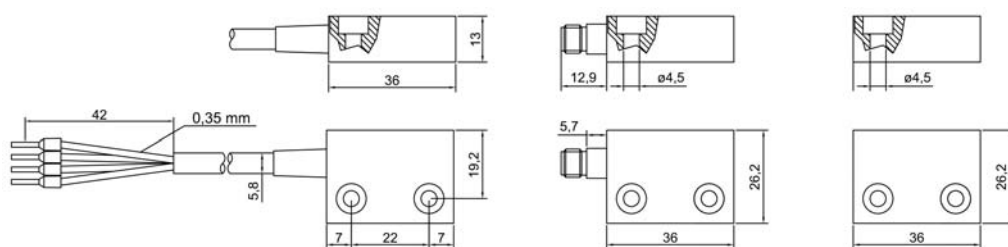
Dimensioni sensore ed attuatore MC336x
